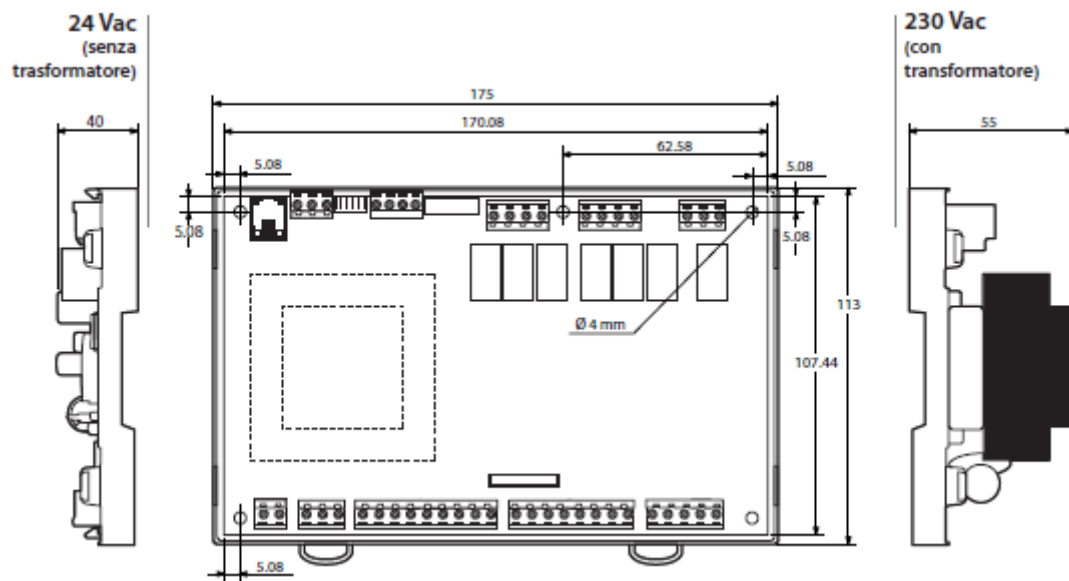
Dimensioni della scheda elettronica μ PC [26]
